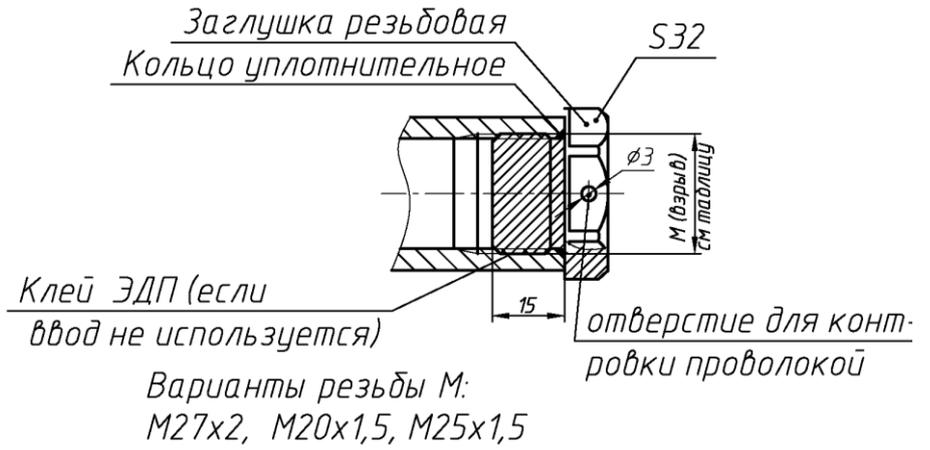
Элементы взрывозащиты при поставке оповещателя с резьбовыми заглушками
